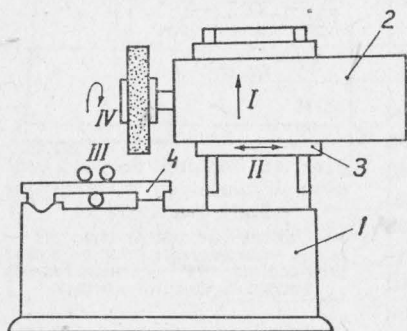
Mașină de rectificat plan orizontal cu păpușă portpiatră deplasabilă transversal:
